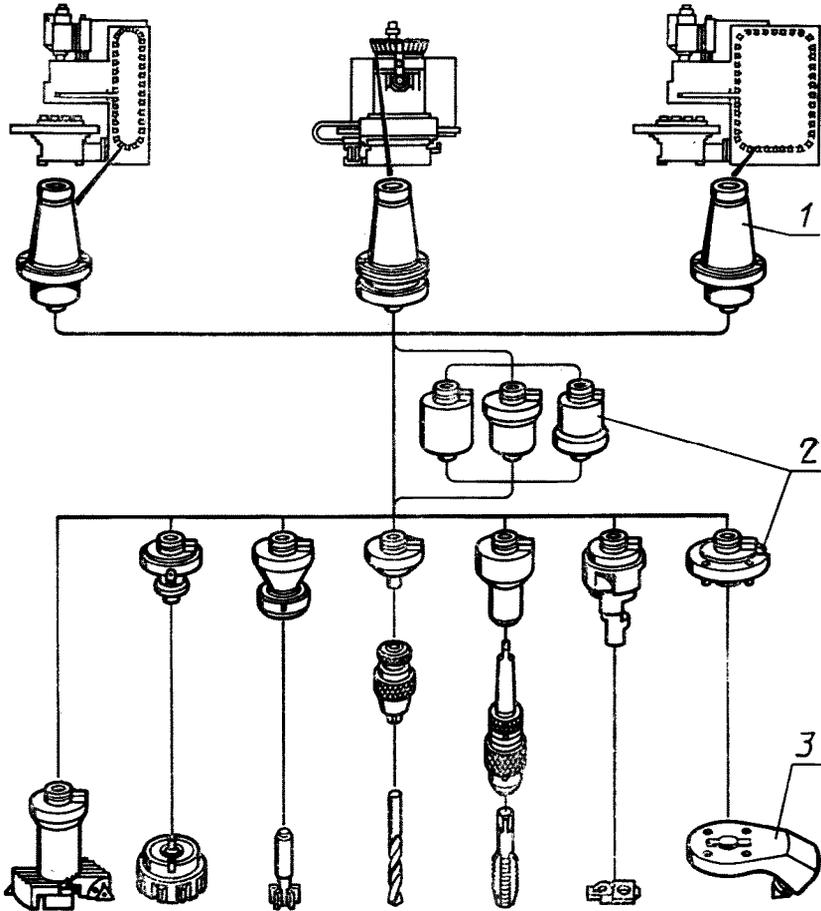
Пример блочно-модульного построения ЦКИ для станков фрезерной группы:
